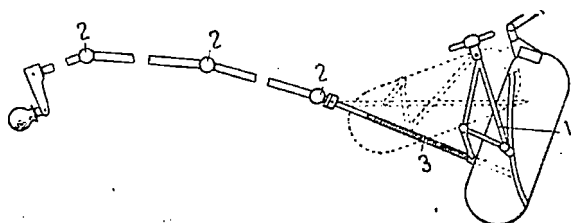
Червячный подъемный механизм радиатора: 1—шатунный механизм; 2—карданные сочленения, 3—червячный винт.
